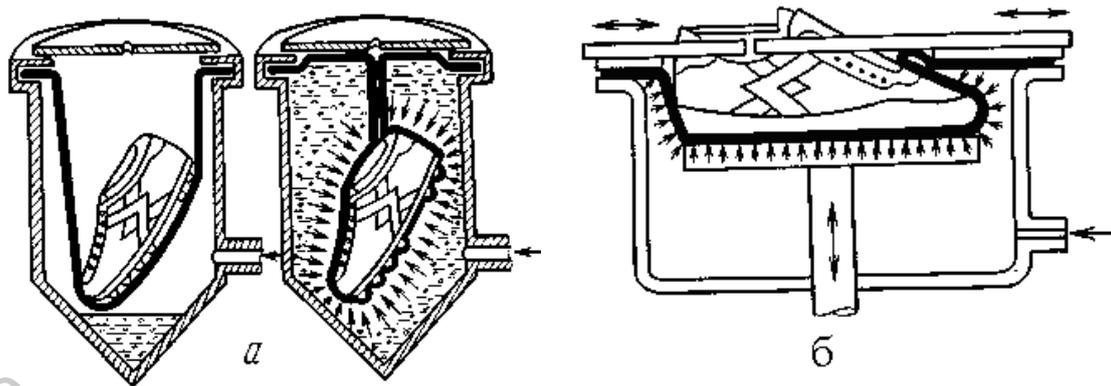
Конструкции пресс-секций прессов камерного типа для приклеивания подошв
